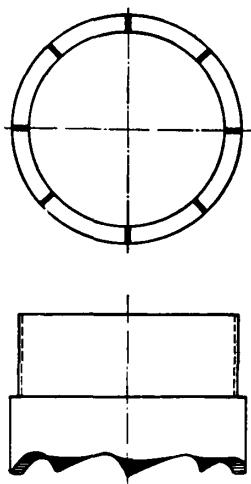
Схема буровой коронки с наваренными зубьями для бурения мерзлых пород, содержащих валуногалечниковый материала
